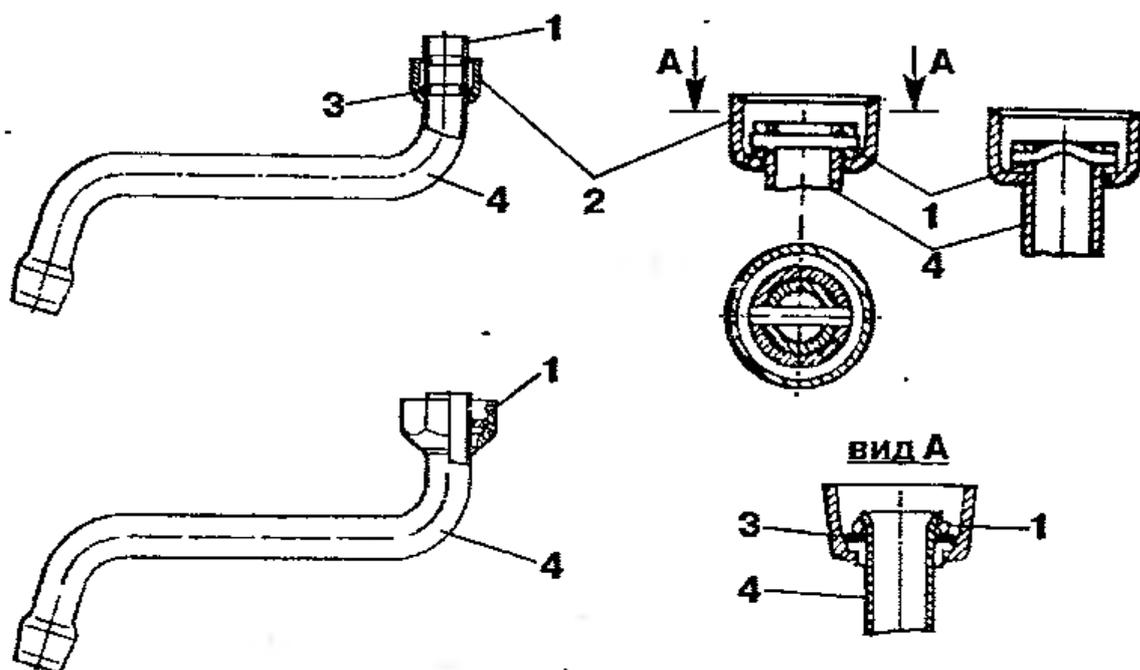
Излив смесителя пробкового типа: 1 — резиновое кольцо; 2 — накидная гайка; 3 — разжимное пластмассовое кольцо; 4 — трубка
